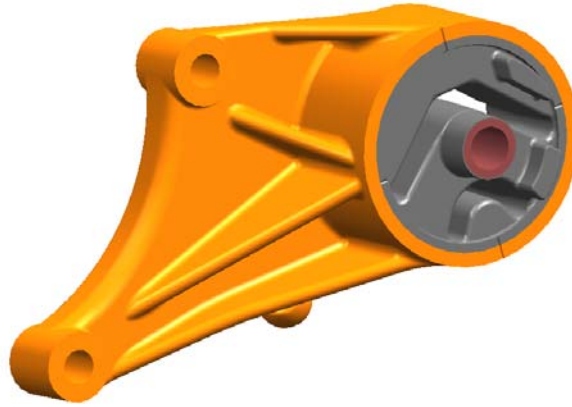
Imagem do coxim de motor de carro de passeio.
